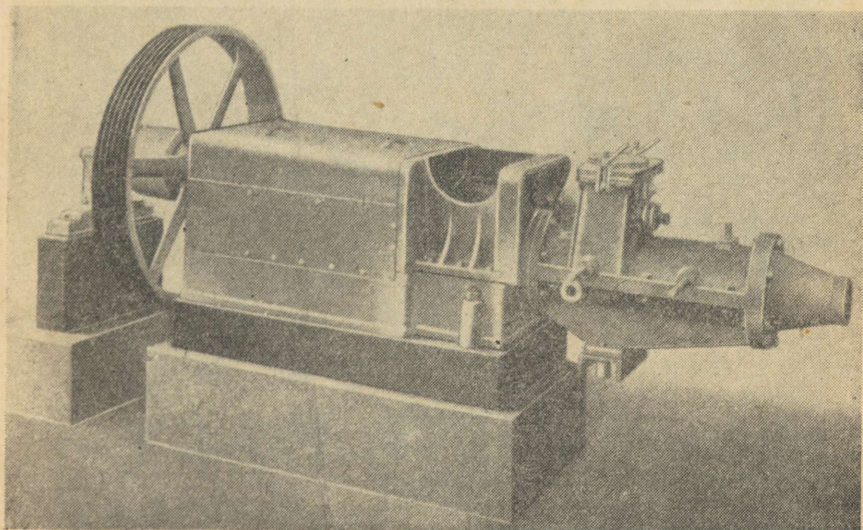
Ленточный вакуум-пресс со ступенчатым шнеком, диаметр цилиндра 180 мм.
